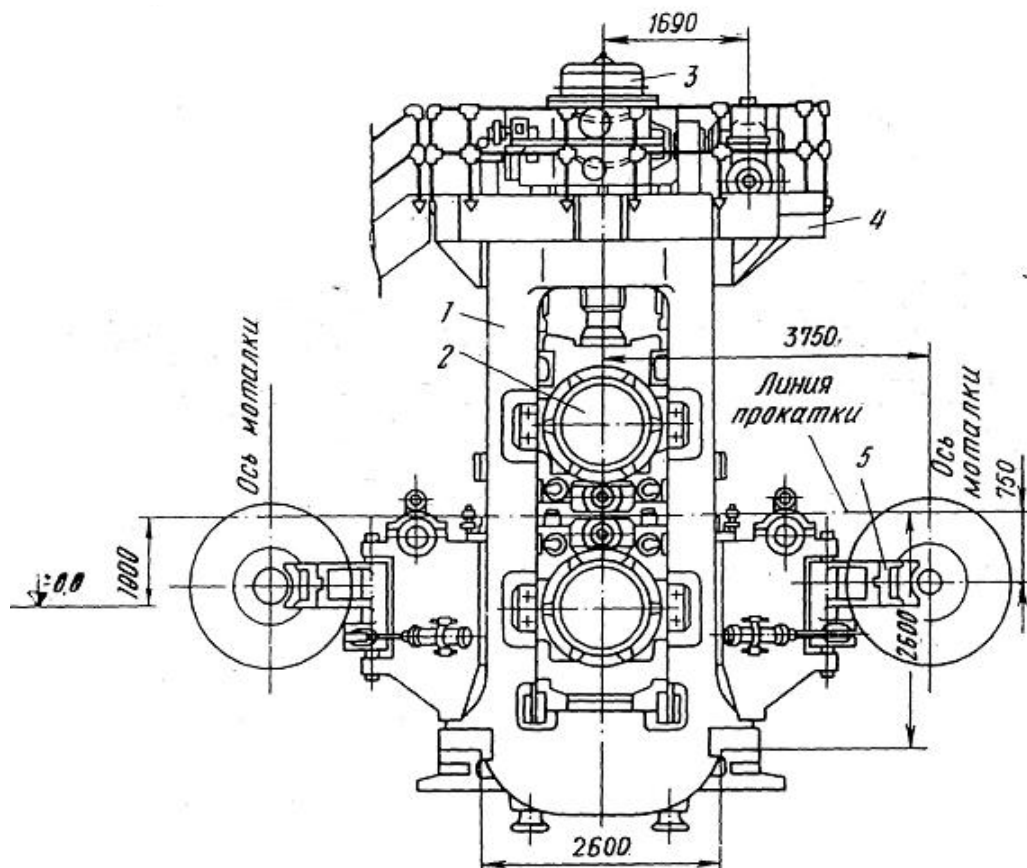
Загальний вид реверсивного стану 1680.
